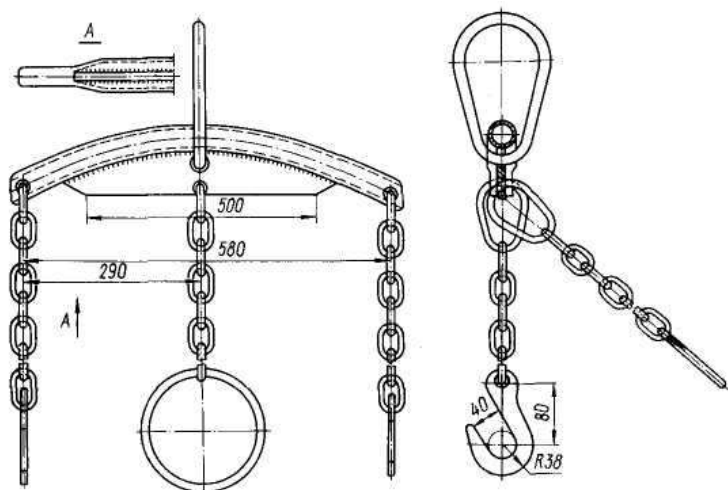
Приспособление для подвески силового агрегата или двигателя к подъемному устройству
